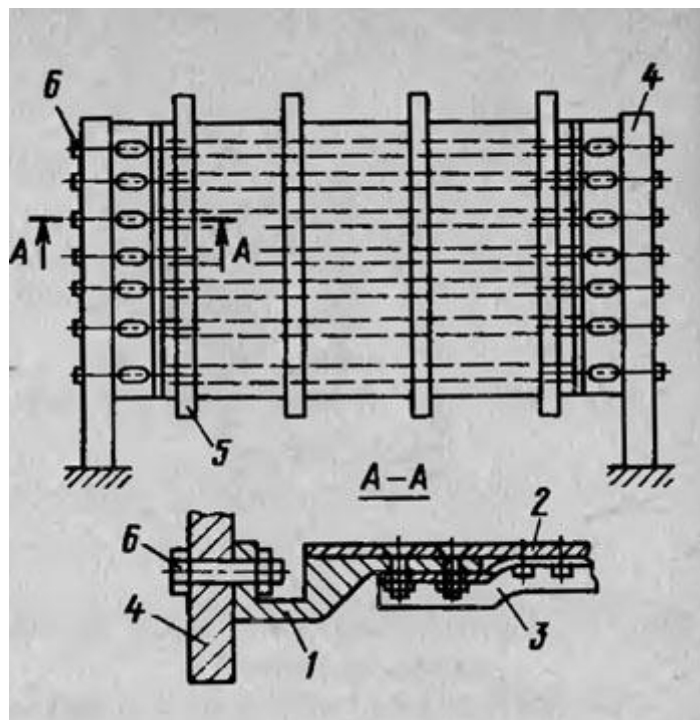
Схема сборки с базированием по отверстиям под стыковые болты: 1 – профиль разъема; 2 – обшивка; 3 – панель; 4 – плита приспособления; 5 – ложемент; 6 – стыковой болт
